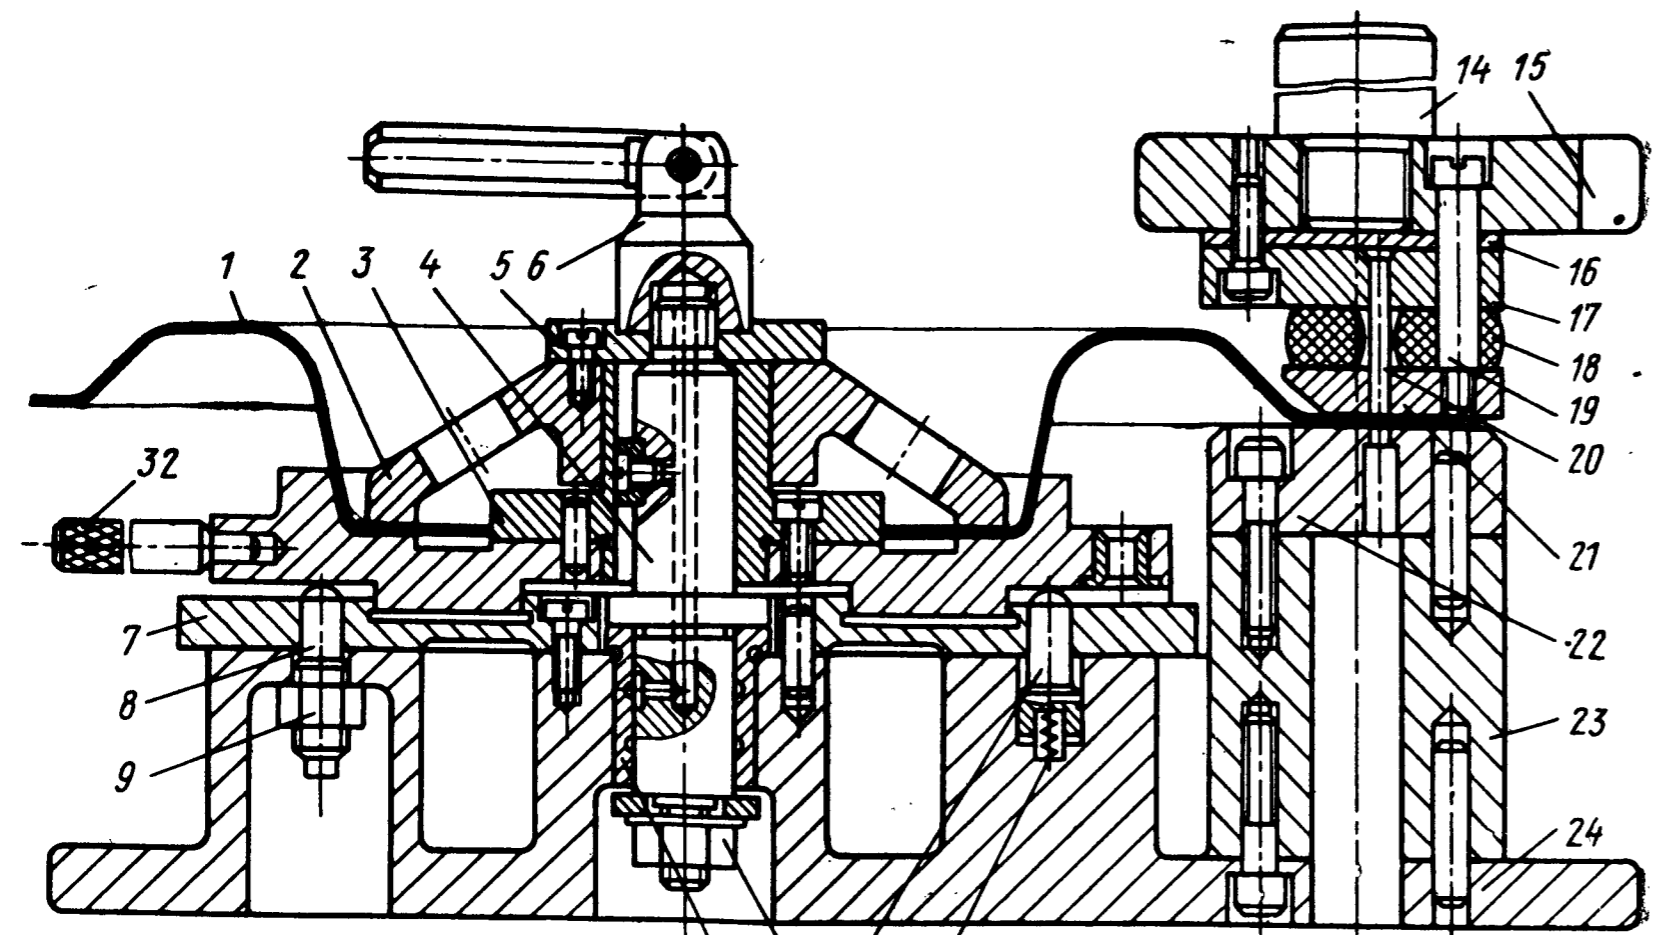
Штамп для пробивки отверстий в кольцевой детали V-образного профиля
